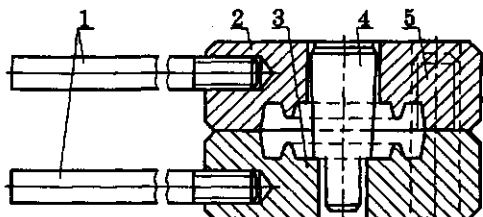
Штамп для восстановления зубчатых колес вдавливанием:
